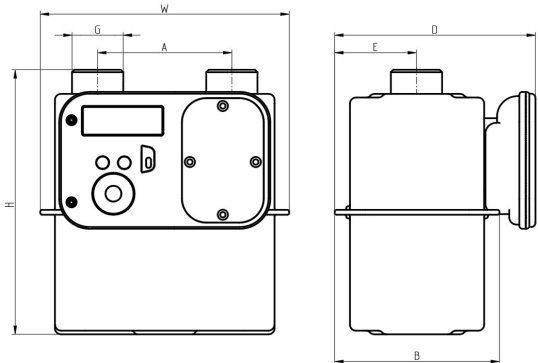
Габаритные и присоединительные размеры счетчиков
